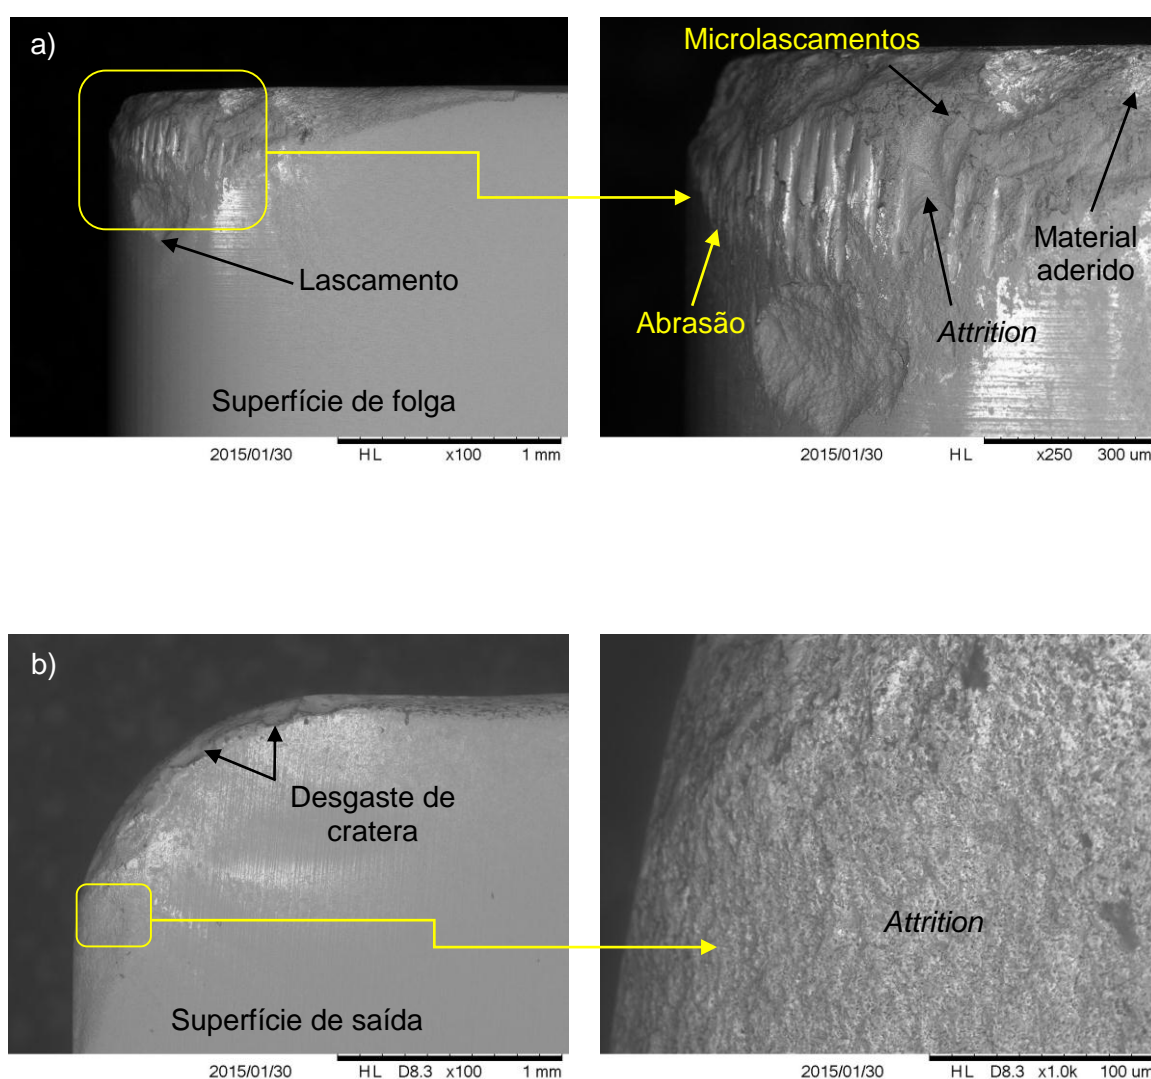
Fotografias obtidas através do MEV das ferramentas SiAlON após a usinagem do Inconel 718 a seco. (a) superfície de folga e (b) superfície de saída
